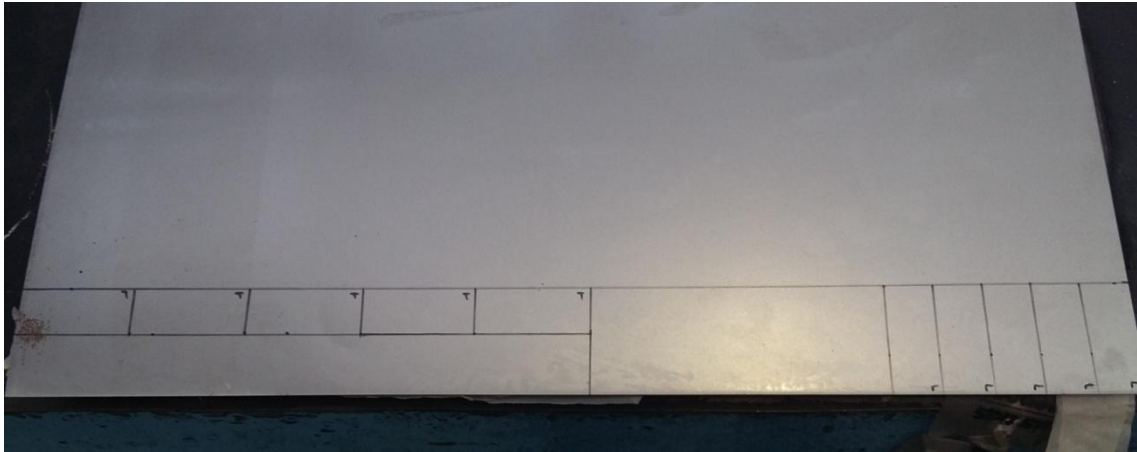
Marcado de las probetas L y T en plancha de acero.
